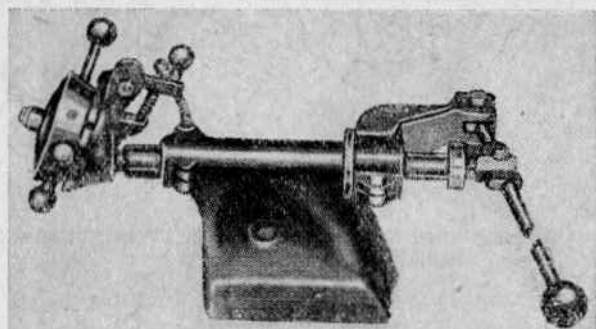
Револьверная головка на шесть гнезд, устанавливаемая в шпindle задней бабки токарного станка
